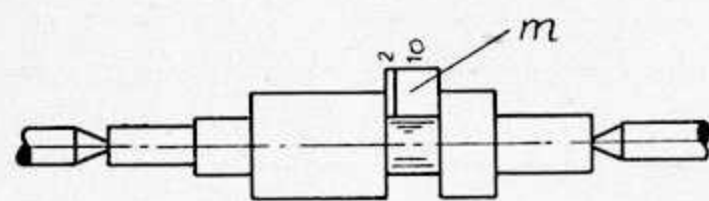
Měření hloubky zápichu Johan-sonovou měrkou a vlasovým pravítkem.
